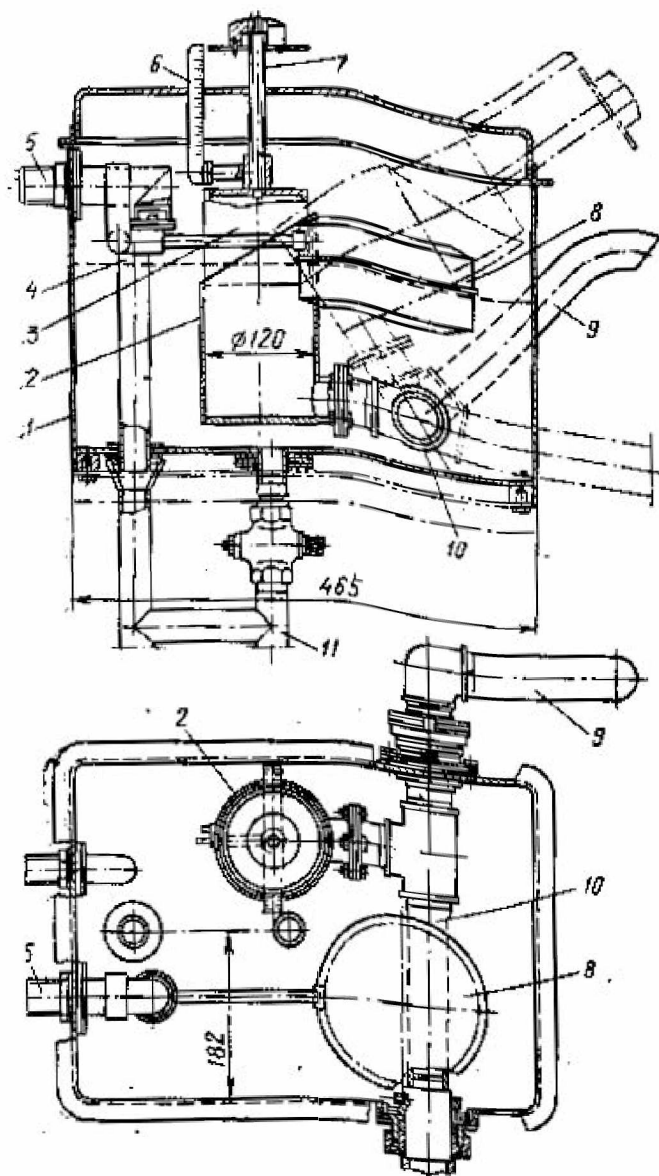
Дозатор черпакового типу: 1 - бак, 2 - мірний стакан; поплавок, 3 - поршень витискач; 4 - переливна труба під кутом 45° , 5 - патрубок подавання рідини; 6 - шкала; 7 регулювальний гвинт; 8 - поплачковий клапан; 9 - зливна труба; 10 - пустотілий вал; 11 - патрубок для зливання рідини підчас промивання
